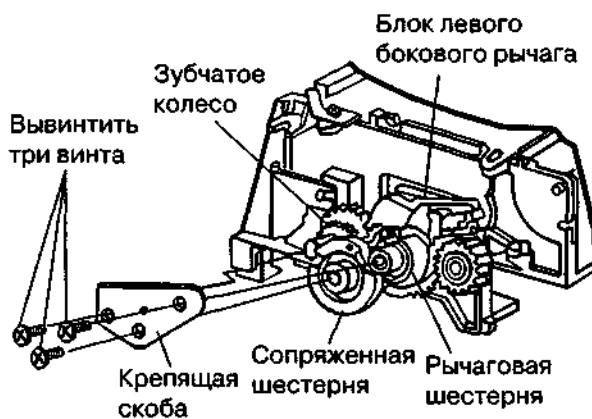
Демонтаж сопряженной шестерни, блока бокового рычага (левого) и червячной шестерни
